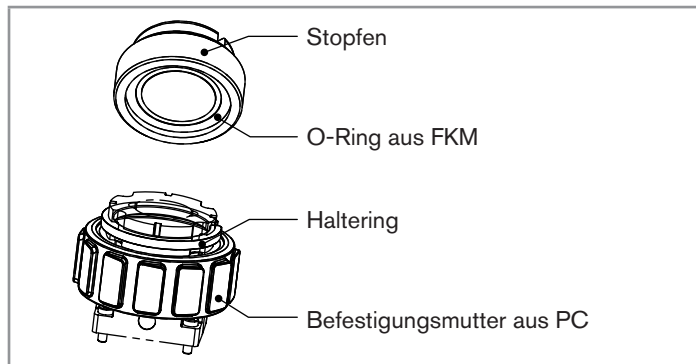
Stopfen mit O-Ring, Befestigungsmutter und Haltering
